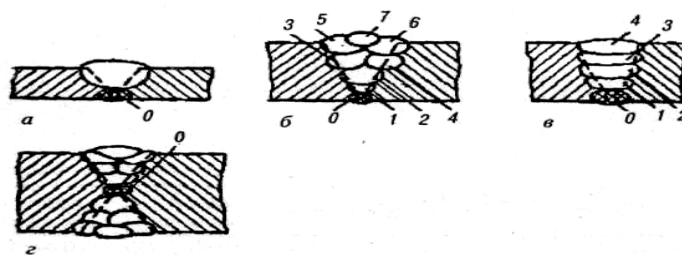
Сварка стыковых швов: а-з – формы поперечных сечений швов; 1-7 – порядок выполнения слоев шва; 0 – подварочный шов
